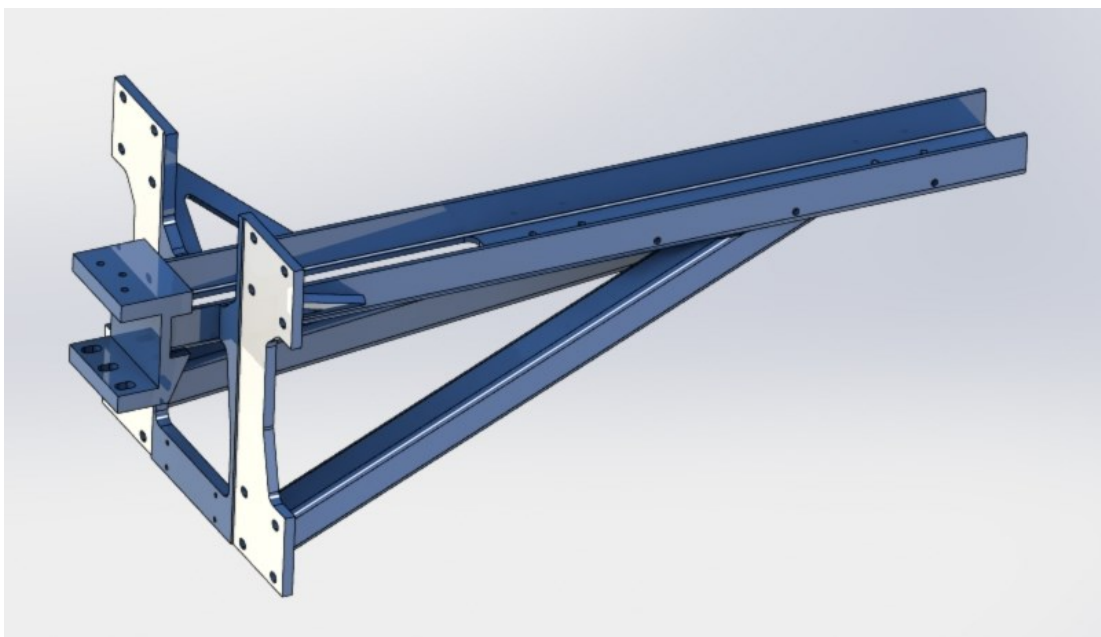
efektor odebrání odpadu a gripper MGP803NC [24]
